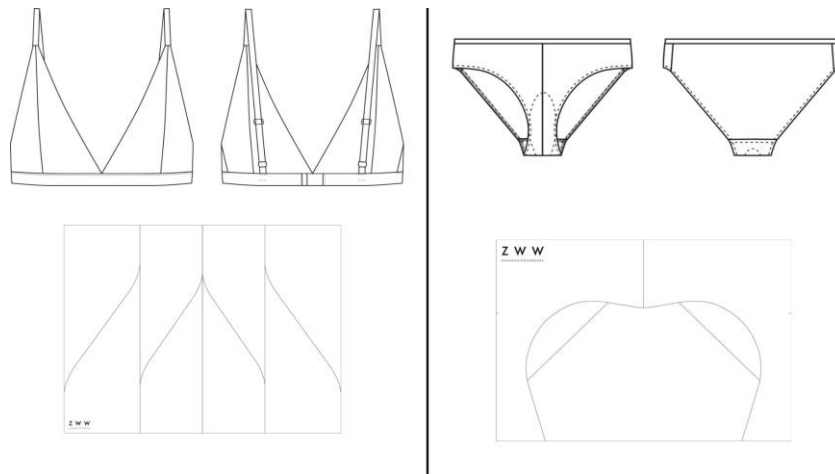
Desenho técnico e molde do sutiã à esquerda desenho técnico e molde calcinha. fonte: *Zero Waste Wardrobe* (2022)
